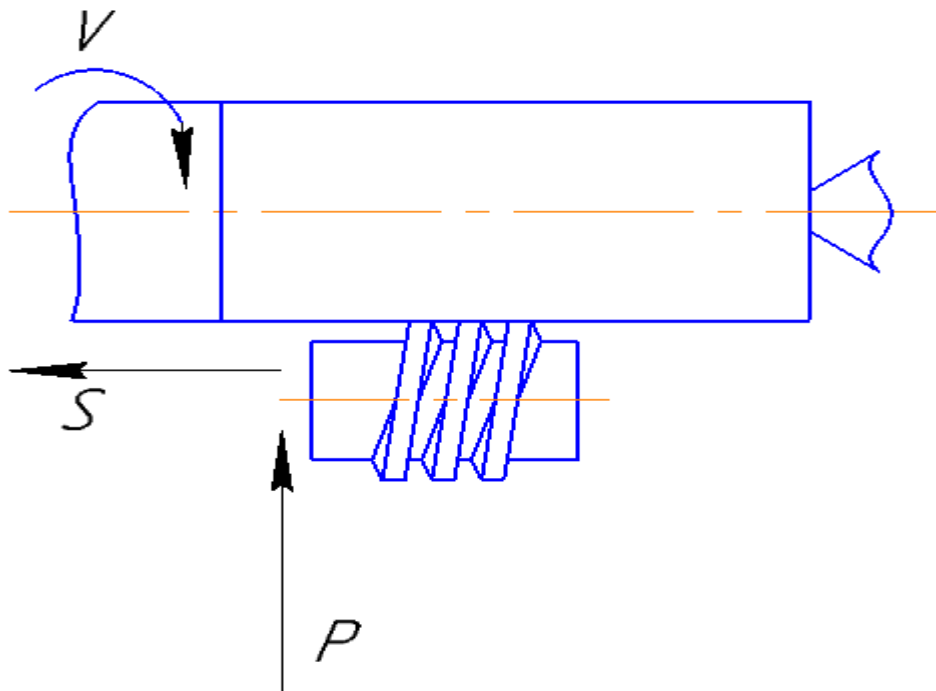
Схема обробки поверхні гвинтовим накатником
